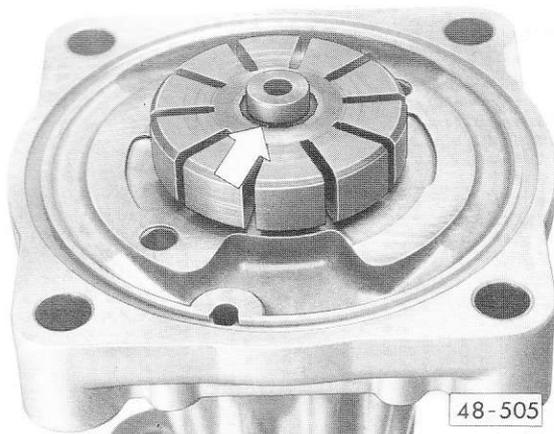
Pour remplacer la bague-joint/ l'arbre de pompe, déposer le rotor et l'arbre de pompe
